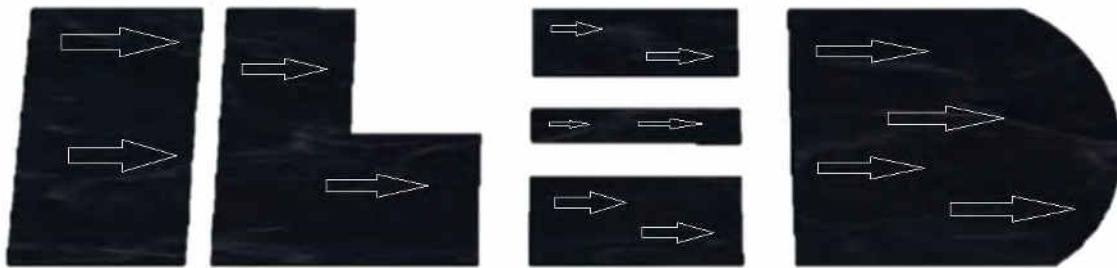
Richtungsmarkierungen auf Aderdekoren vor dem Schneiden
